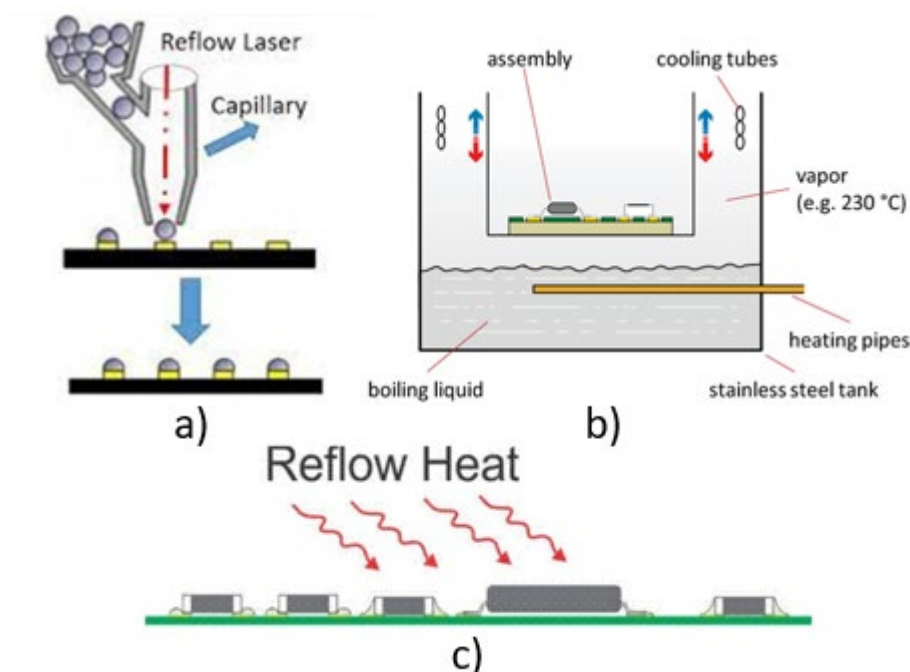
Equipamentos de soldadura comumente utilizado.[43]
